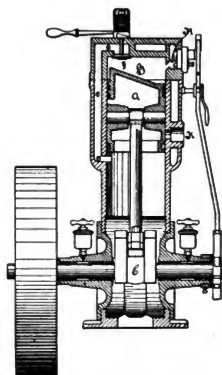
Schnitt durch den Zylinder des Smalley-Motors.
